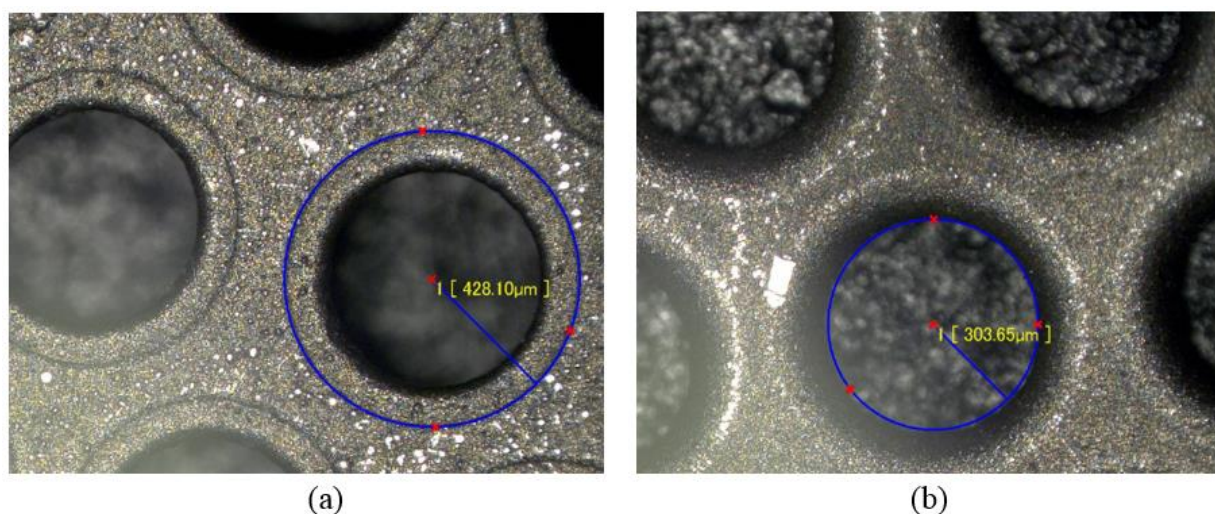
Grille fine de 0,2 mm d'épaisseur : (a) vue de dessus; (b) vue de dessous
